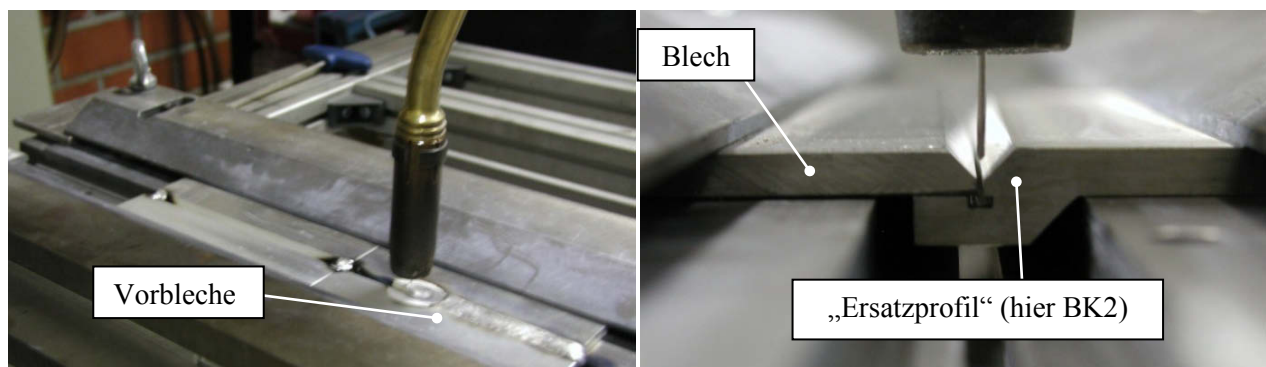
Verschweißen der Bleche und Ersatzprofile im Schweißlabor
